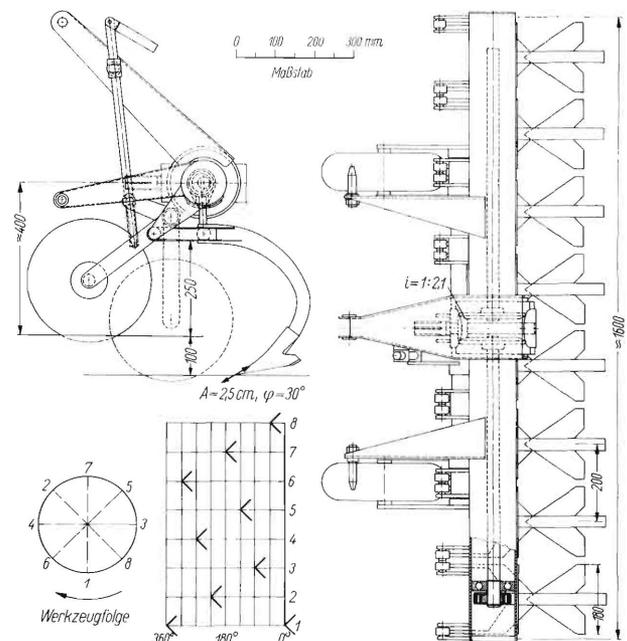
Grubber mit schwingenden Werkzeugen mit Schema der Werkzeugfolge.
